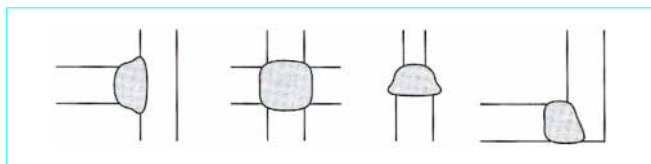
Possibilités d'assemblage par soudage vertical sous laitier
